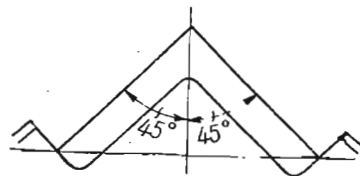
Расположение в вальках калибров для прокатки равнобокой угловой стали
